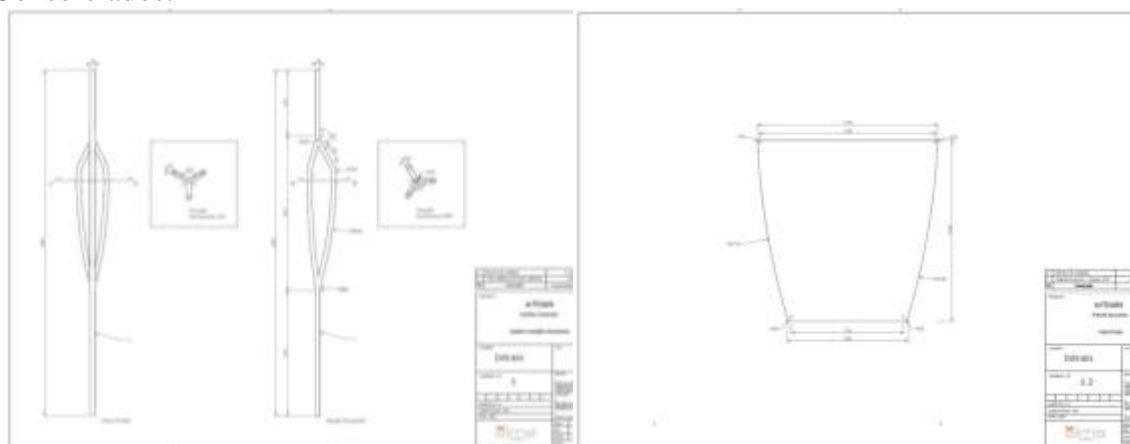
Desenhos Técnicos de componentes e material de acabamento
